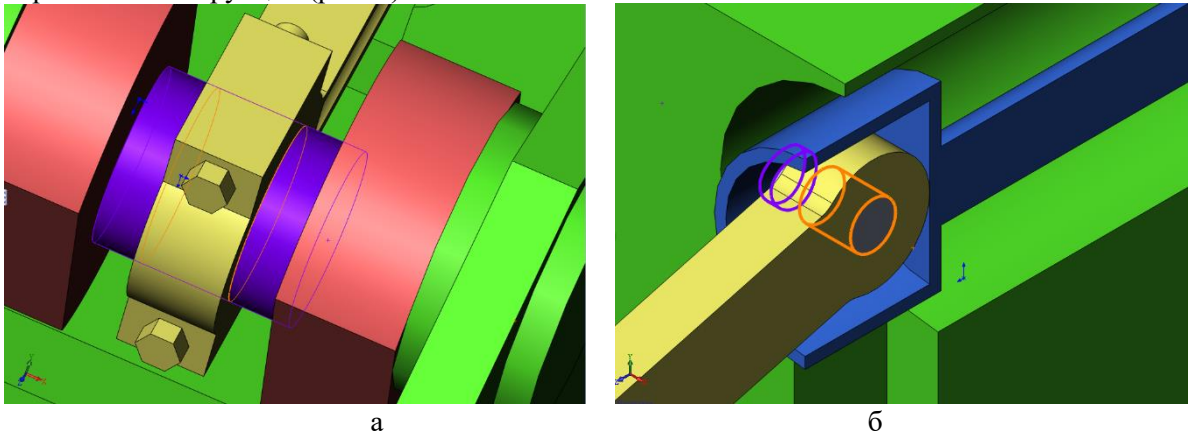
Процесс сборки: а) коленчатого вала и шатуна; б) шатуна и поршня
